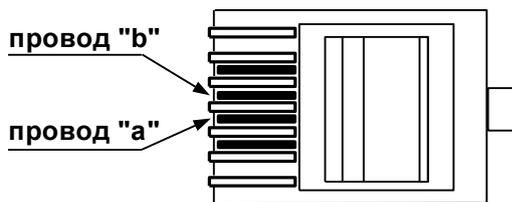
Схема монтажа проводов в вилке 5-0641335-3 AMP
